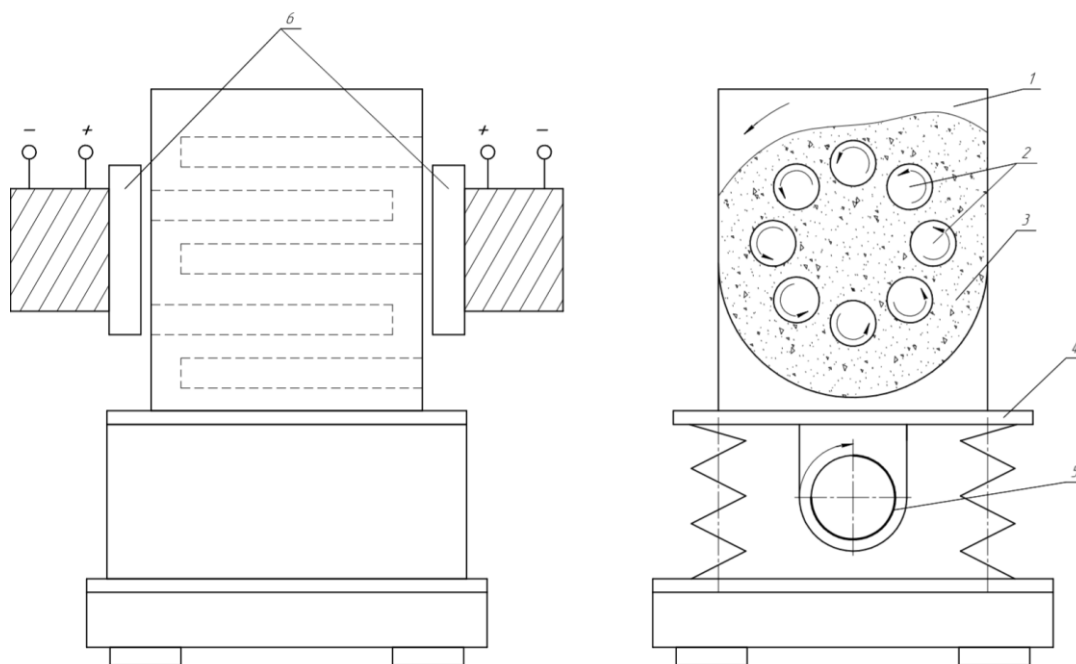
Схема устройства для магнитно-виброабразивной обработки: 1 – контейнер; 2 – ферромагнитные детали; 3 – рабочая среда; 4 – подвижная платформа; 5 – вибратор; 6 – электромагниты
